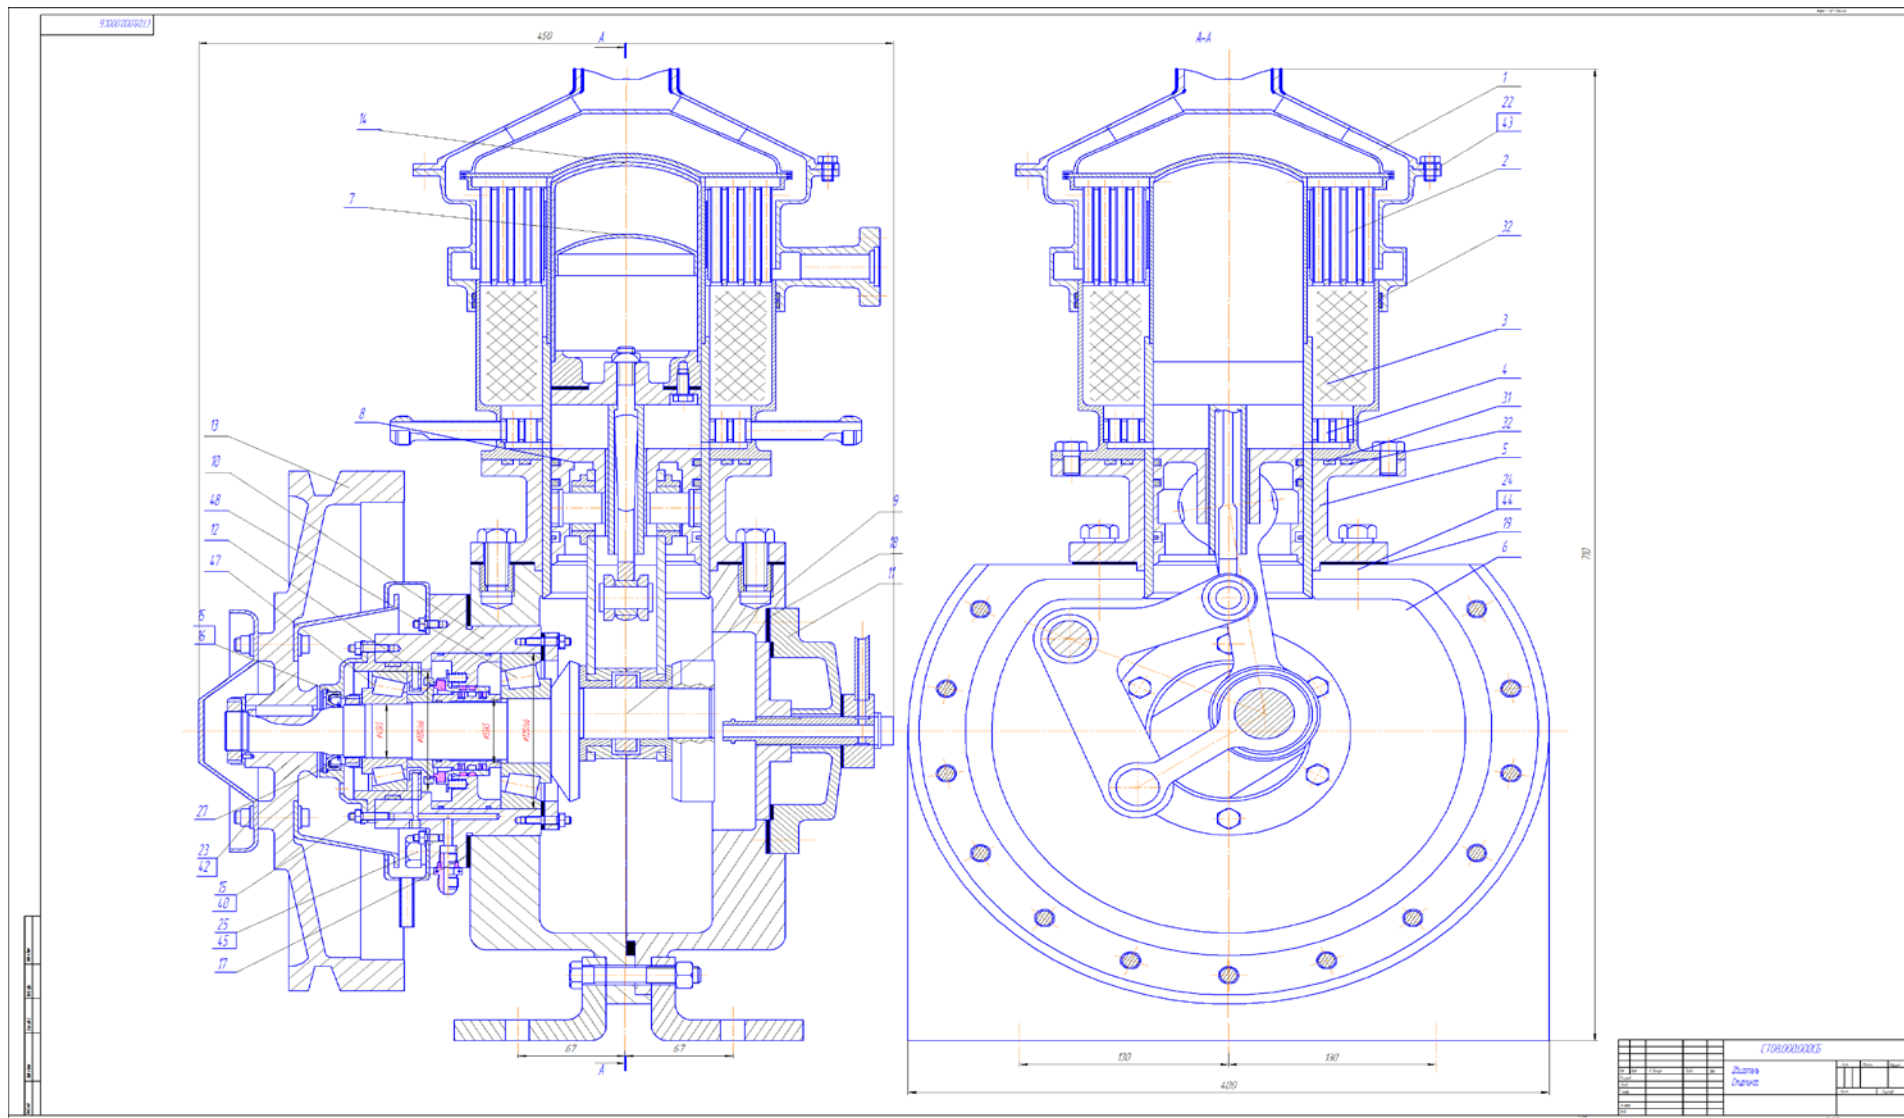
Продольный и поперечный разрез двигателя Стирлинга
